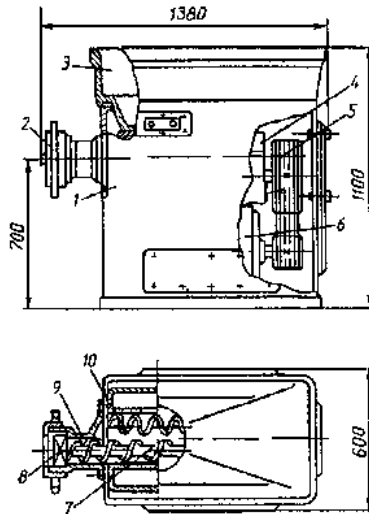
Вовчок МП-1-160: 1 - станина; 2 - накидна гайка; 3 - завантажувальна горловина; 4 - редуктор; 5 - клинопасова передача; 6 - електродвигун; 7, 10 - подавальний й живильний шнеки; 8 - ріжучий механізм; 9 - циліндричний корпус
